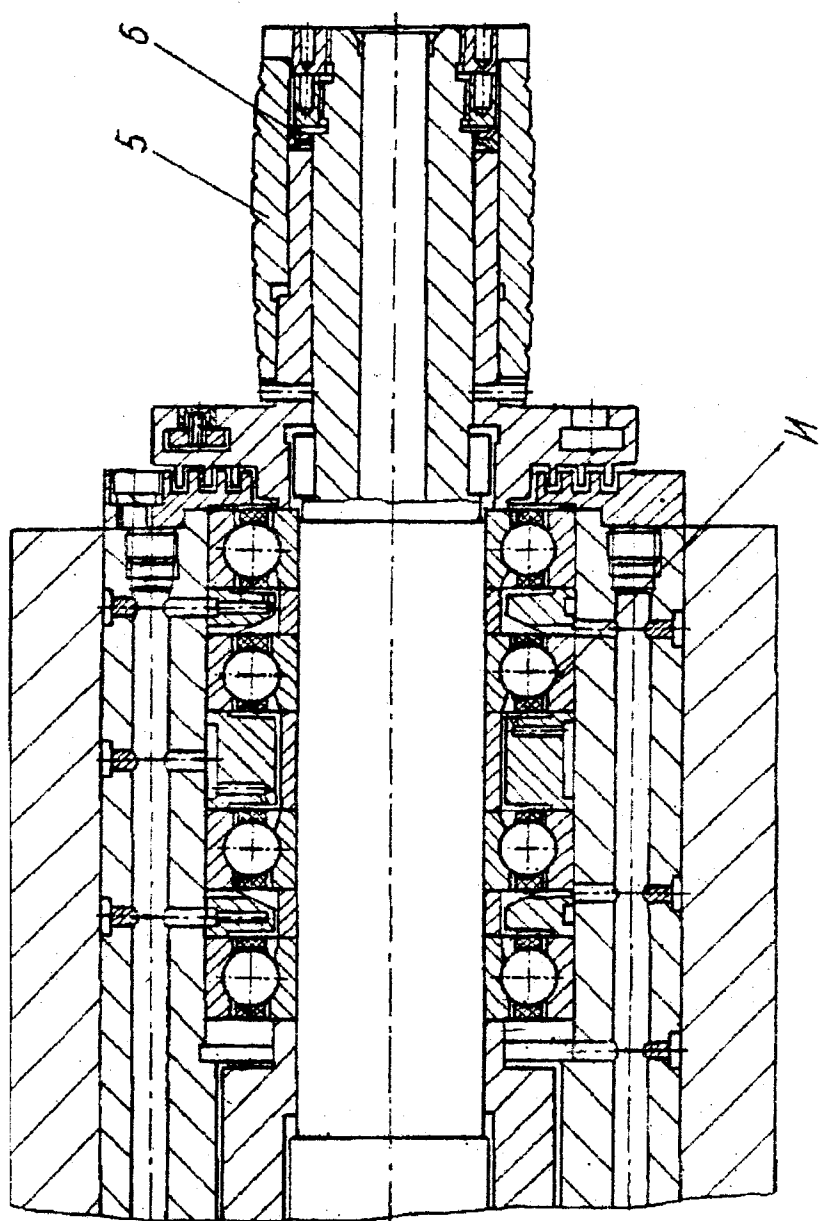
Задняя опора шпинделя внутришлифовального станка
